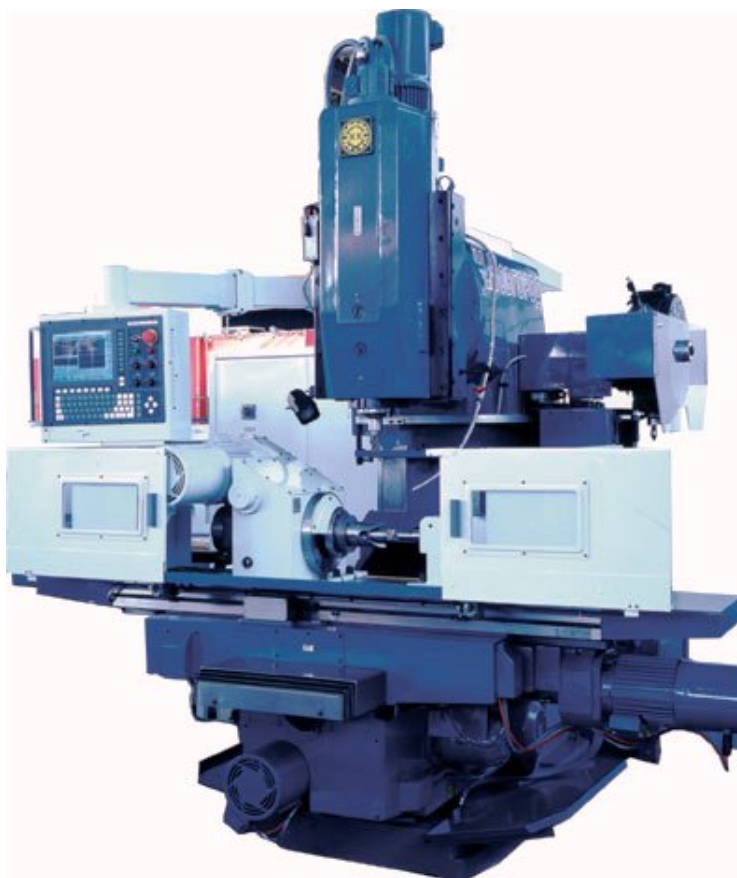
Вертикально-фрезерний верстат з ЧПУ ГФ2171М4
